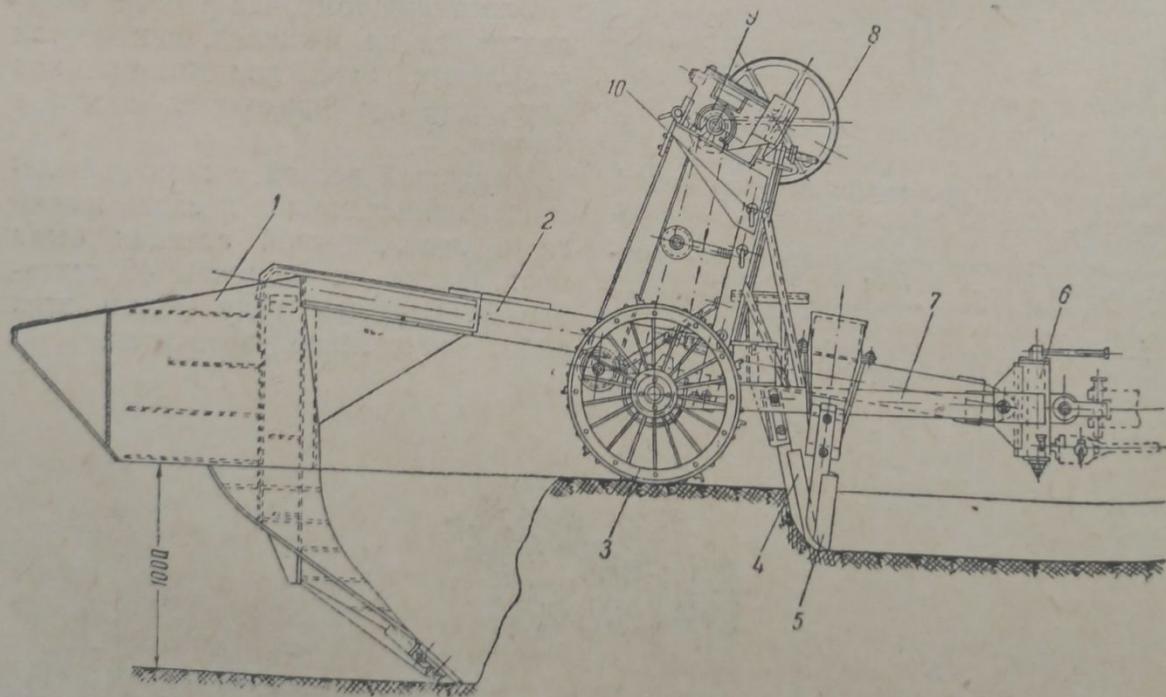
Схематический разрез канавокопателя КМ-1000 А (вид сбоку): 1—корпус, 2—основная рама, 3—ходовое колесо, 4—средний нож, 5—боковой нож, 6—прицеп, 7—ходовая рама, 8—штурвальное колесо, 9—лебедка, 10—фиксатор.
